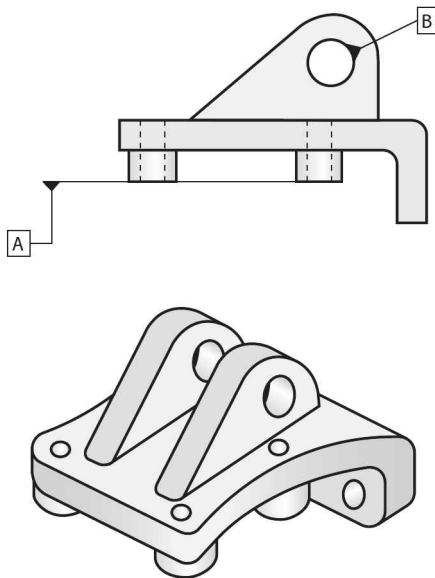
O desenho tem uma referência básica, mas, até que o fundido bruto seja usinado, não existe um lugar confiável para indicar o PZP. Esta peça, idealmente, é posicionada em um gabarito de fresadora.
